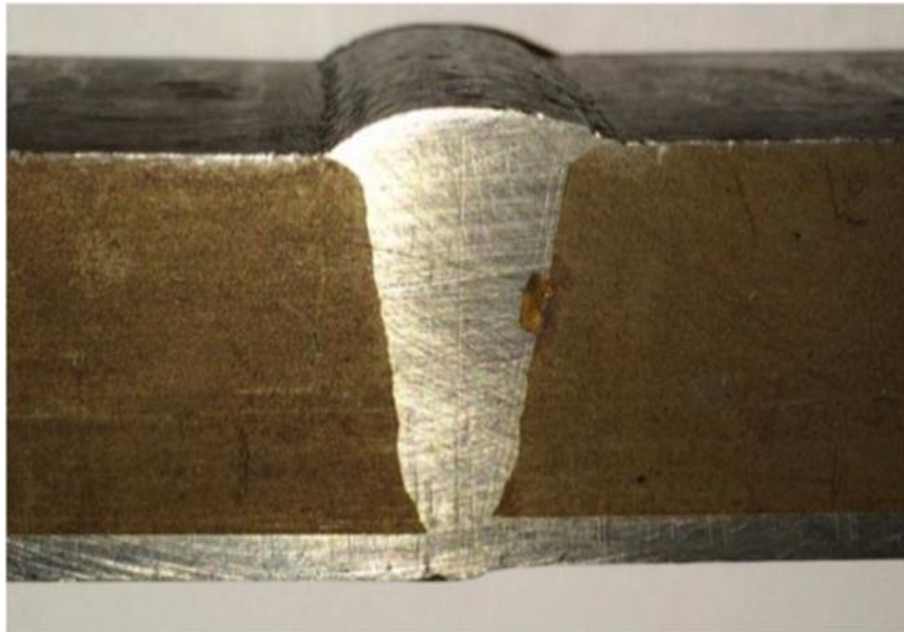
Coupe transversale d'un joint soudée.
